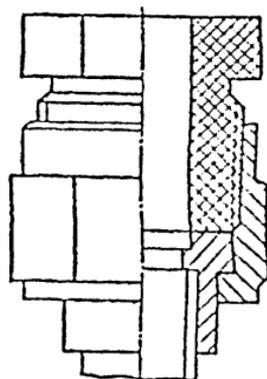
Муфта-заглушка для защиты внутренней резьбы (на пь вершках и накидных гайках с низ пельми) при травлении
